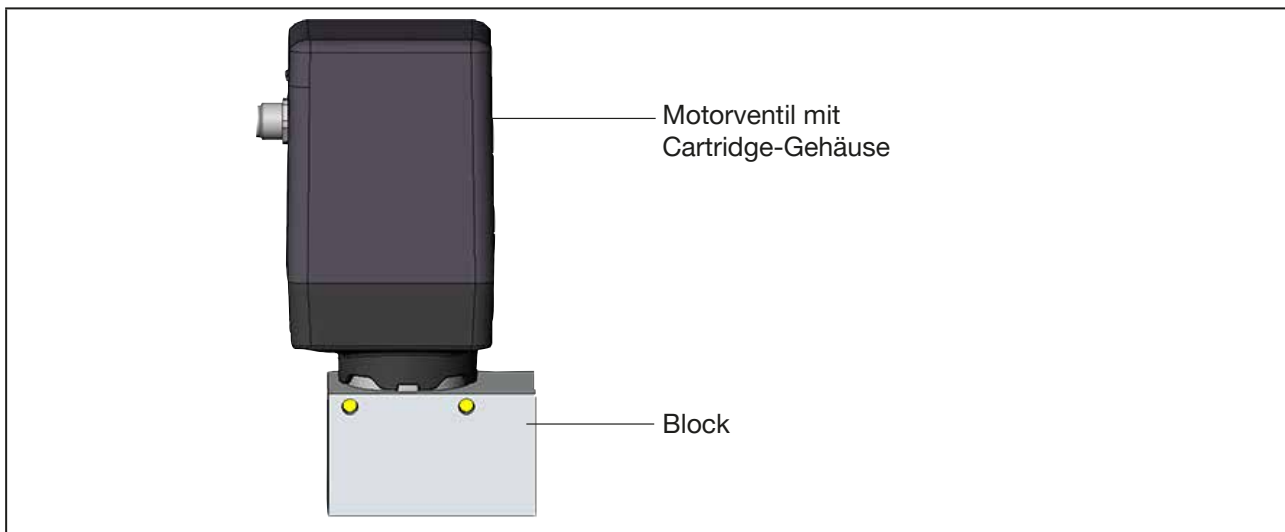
Eingebautes Gerät mit Cartridge-Gehäuse
